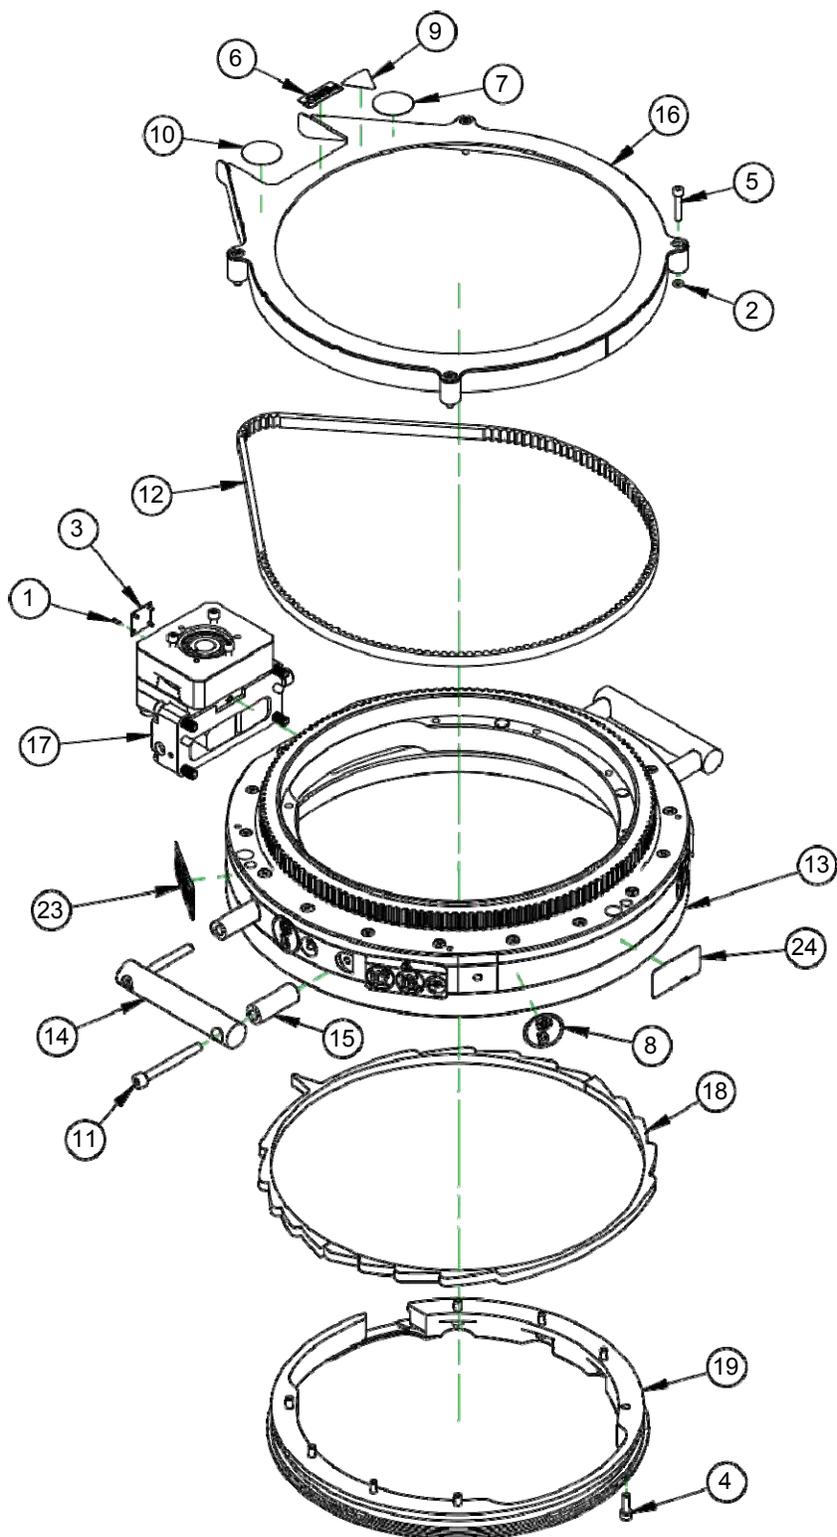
ENSEMBLE DE L'UNITÉ DE COMMANDE ROTATIVE DE LA FF1200 (RÉF. 79752)
